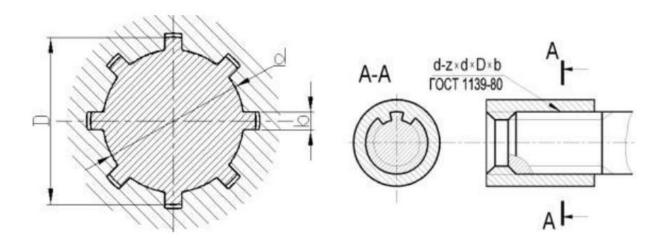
Шлицевое соединение: а) прямобочный профиль шлица; б) изображение и обозначение прямобочного зубчатого соединения.
